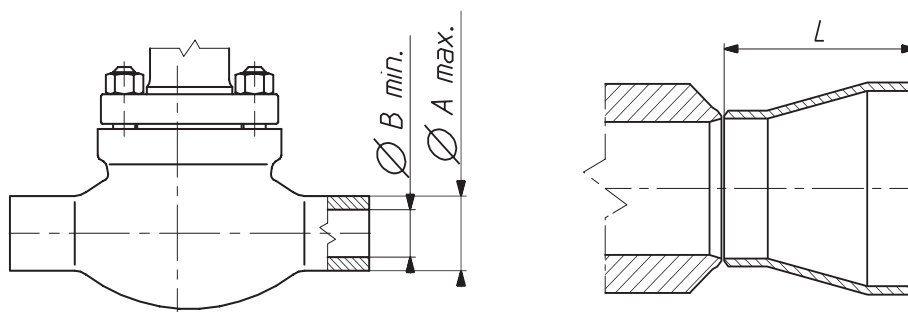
Außen-, Innendurchmesser und Reduzierstücke für Anschweißenden
